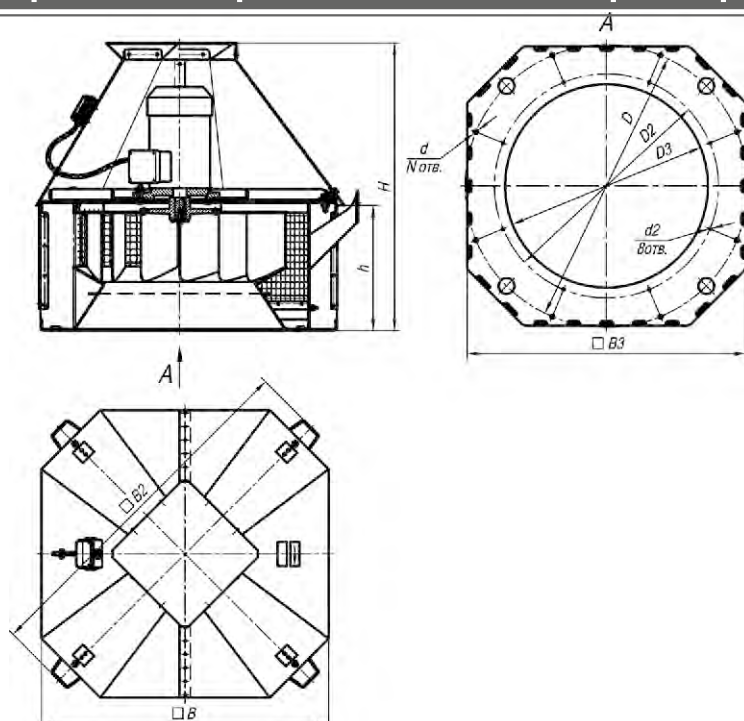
Габаритные и присоединительные размеры ВКРм №3,15-№10 исп-1.
